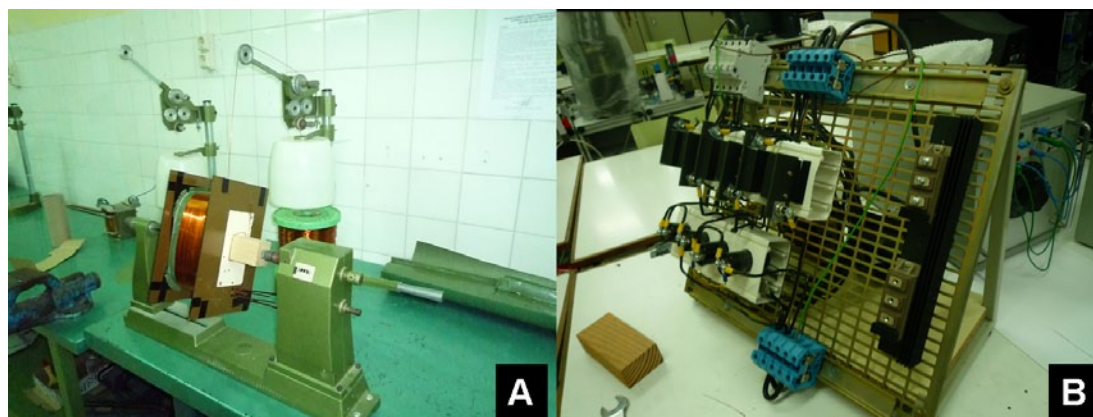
Partes de la máquina de descargas, A. bobinado para construir el transformador, B) aspecto del rectificador y filtro.
